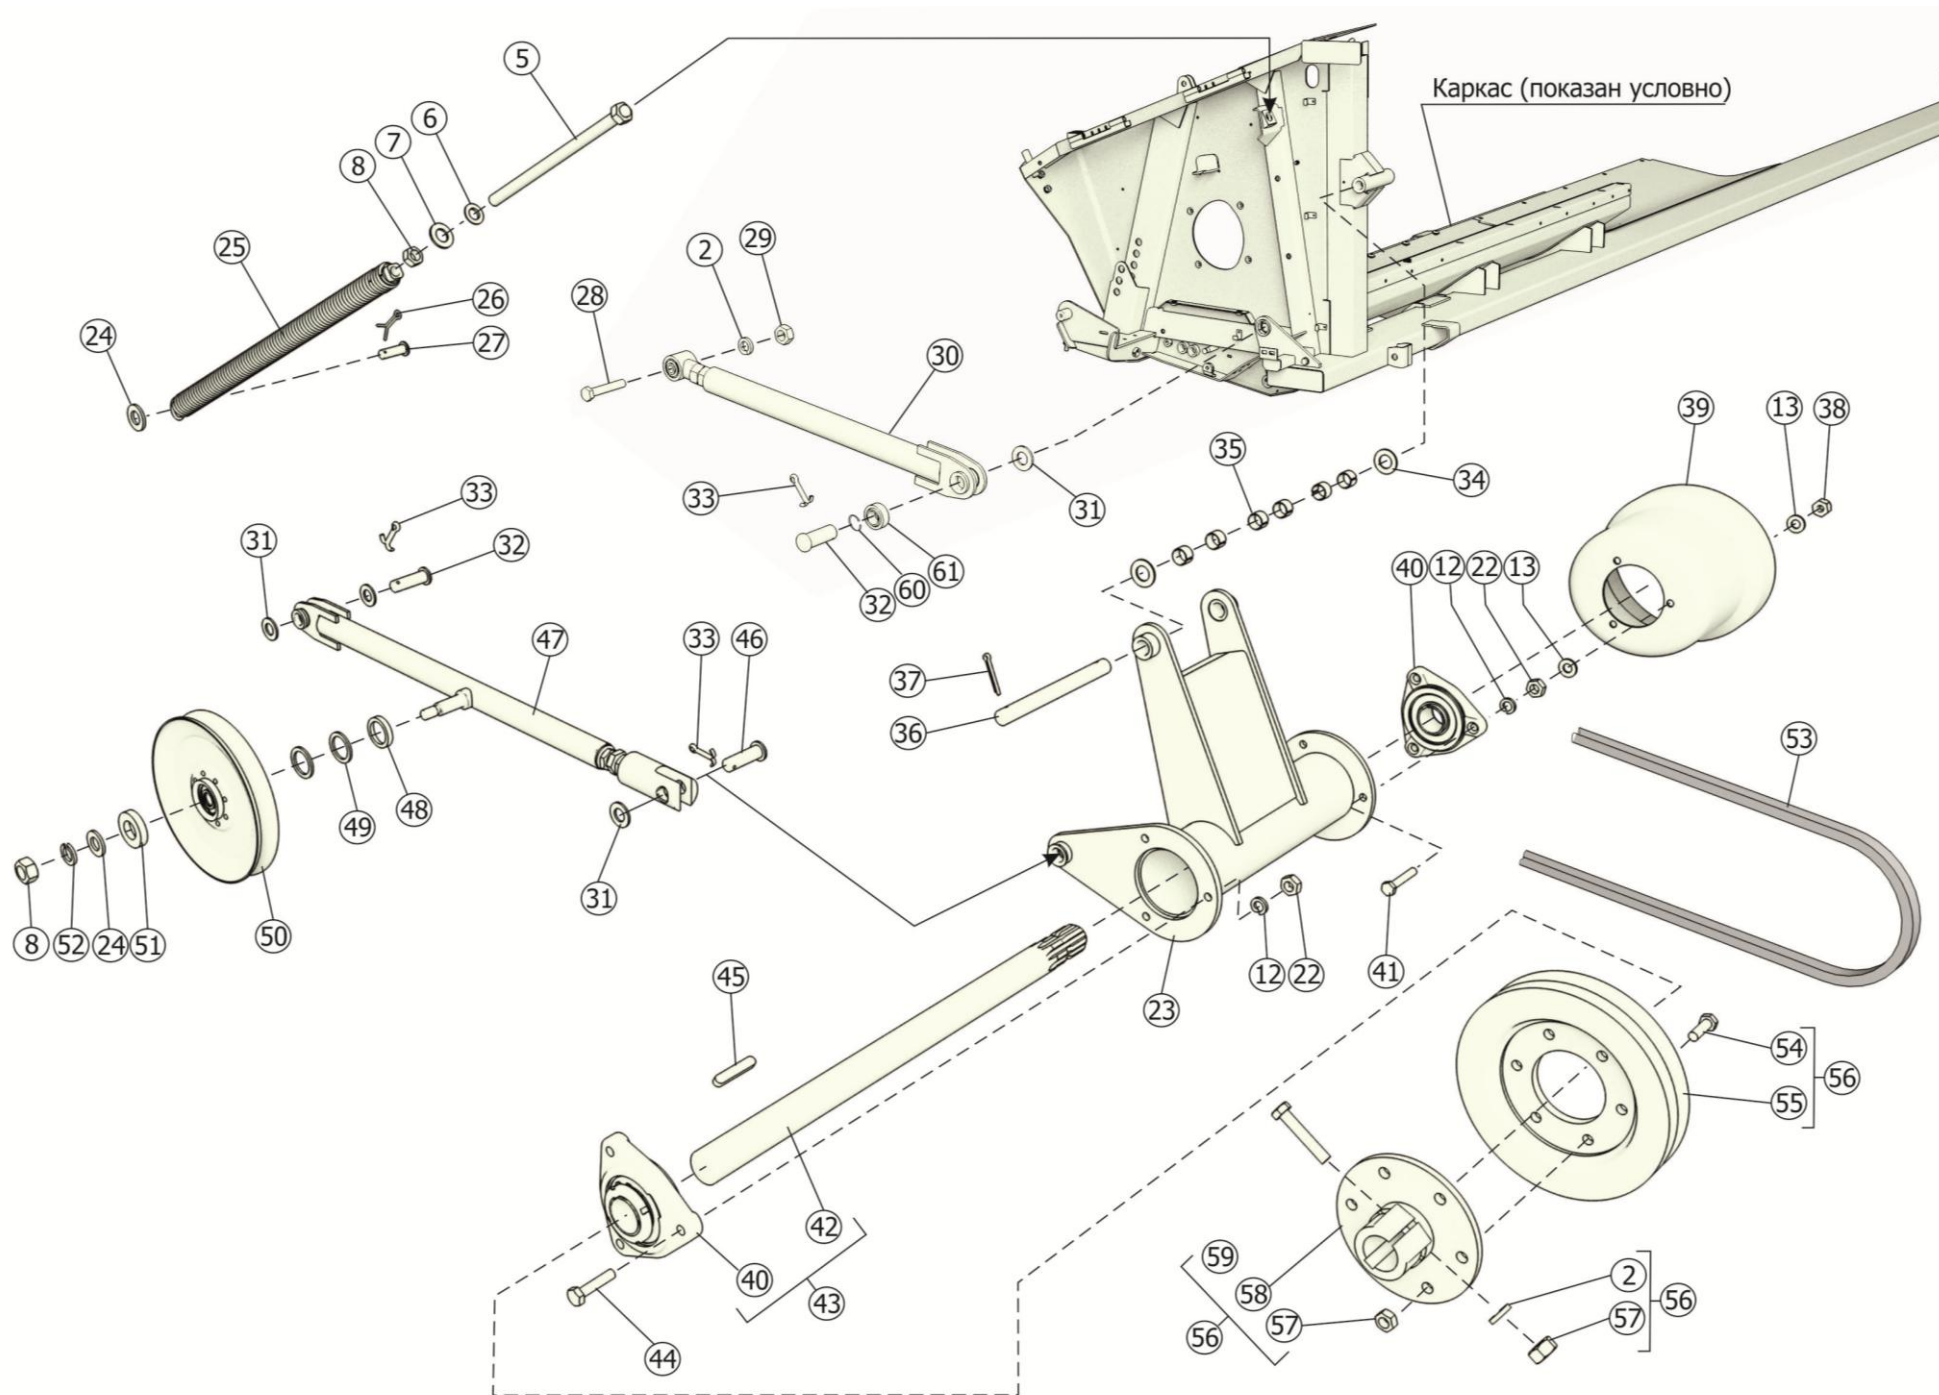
Привод режущего аппарата ЖСУ-703.01.03.500. Вид слева
